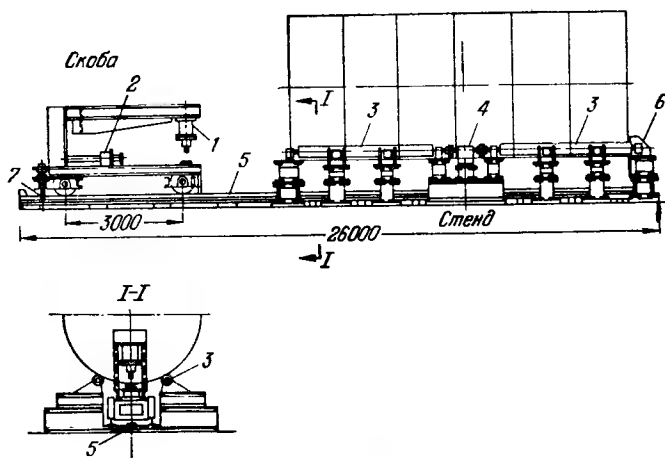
Стенд со сборочной скобой для общей сборки габаритных резервуаров (Кузнецкий и Днепропетровский заводы металлоконструкций)
